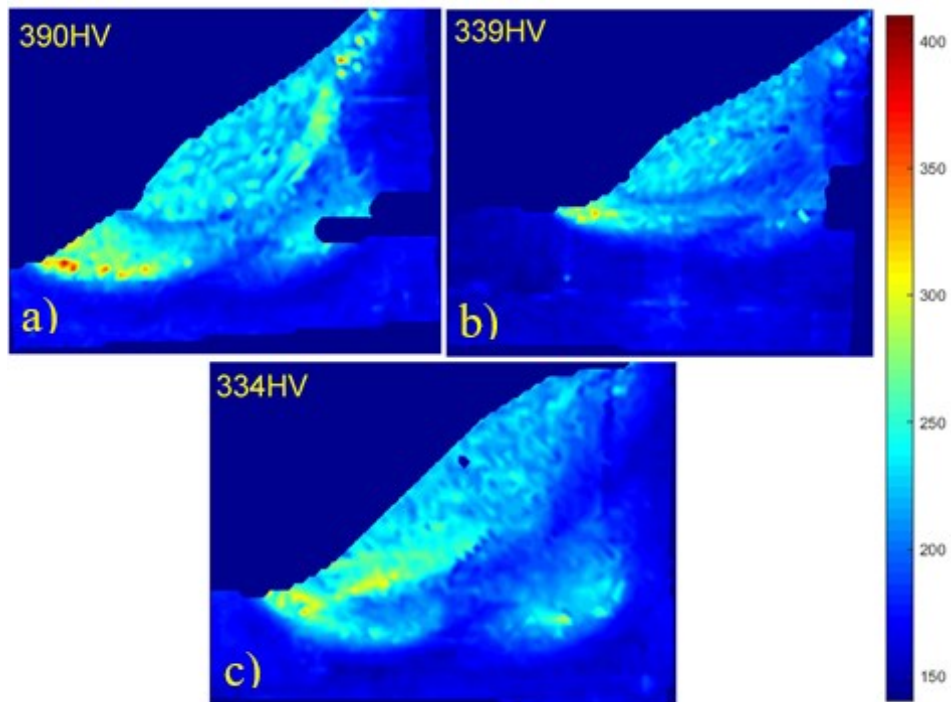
Mapas de microdureza para a soldagem com GMAW-P DC. Em a) Sem aquecimento por indução; b) Com aquecimento da calha; c) Com aquecimento duplo bancada inclinada.
